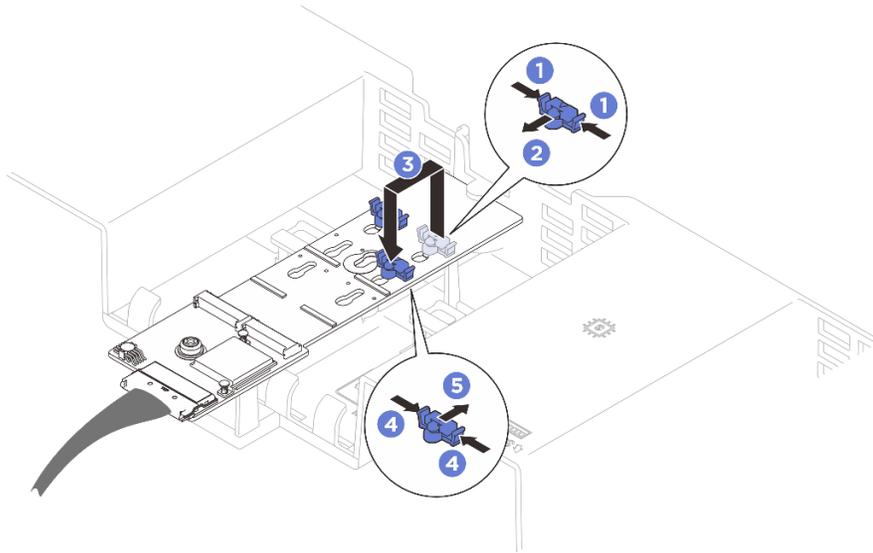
Регулировка положения фиксатора адаптера загрузки M.2
